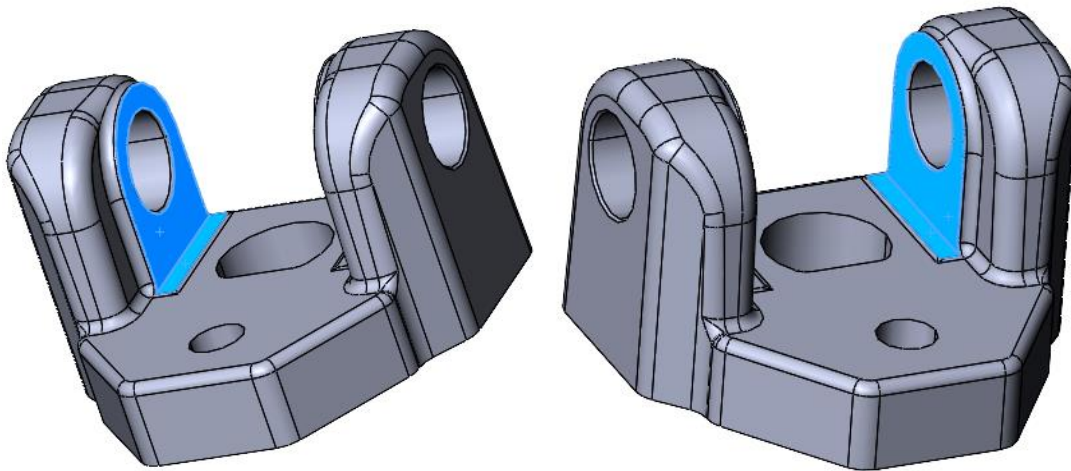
3D- модель деталі з поверхнями для фрезерування на верстаті з ЧПК.
